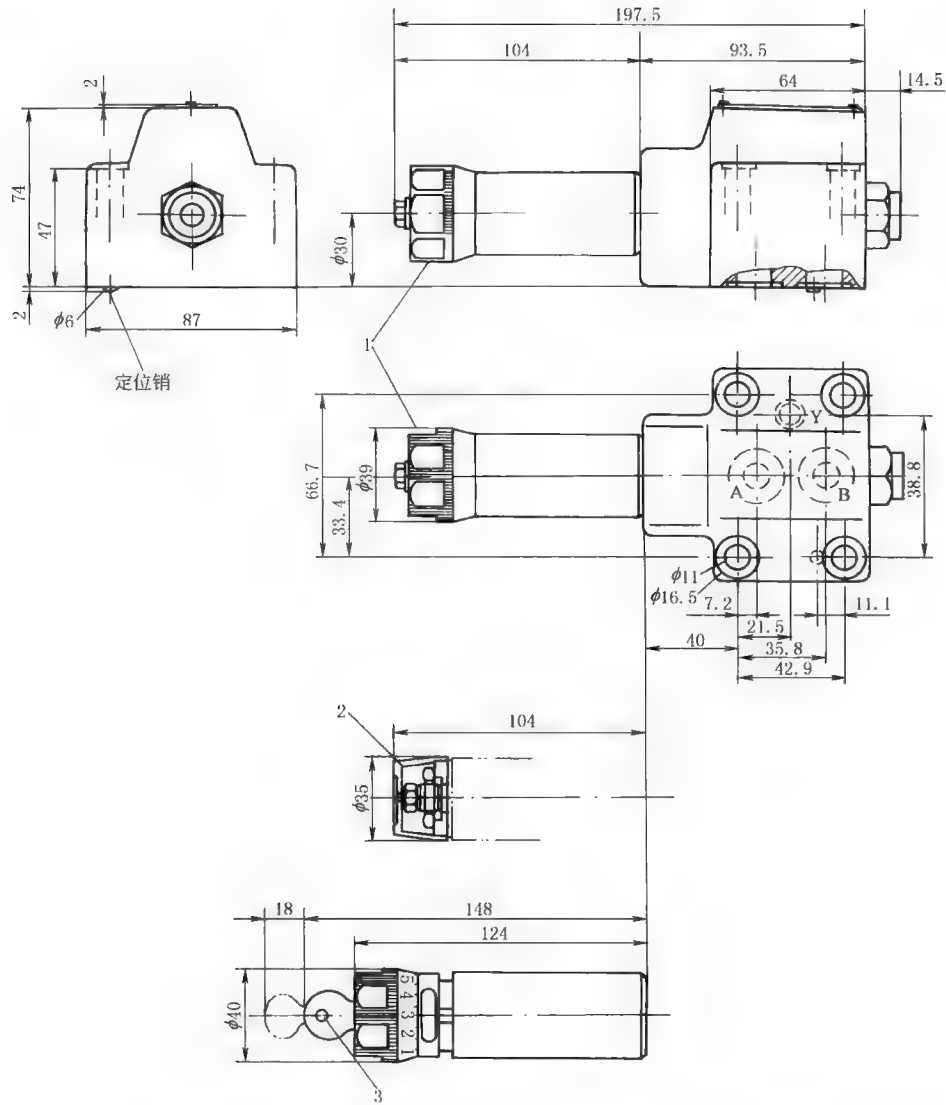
DZ10DP 型直动式顺序阀外形尺寸
